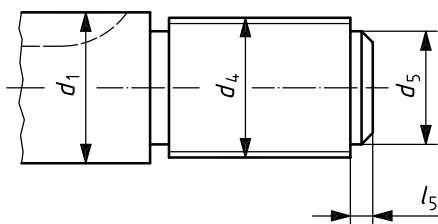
Dimensions de la portée de protection en bout d'arbre
